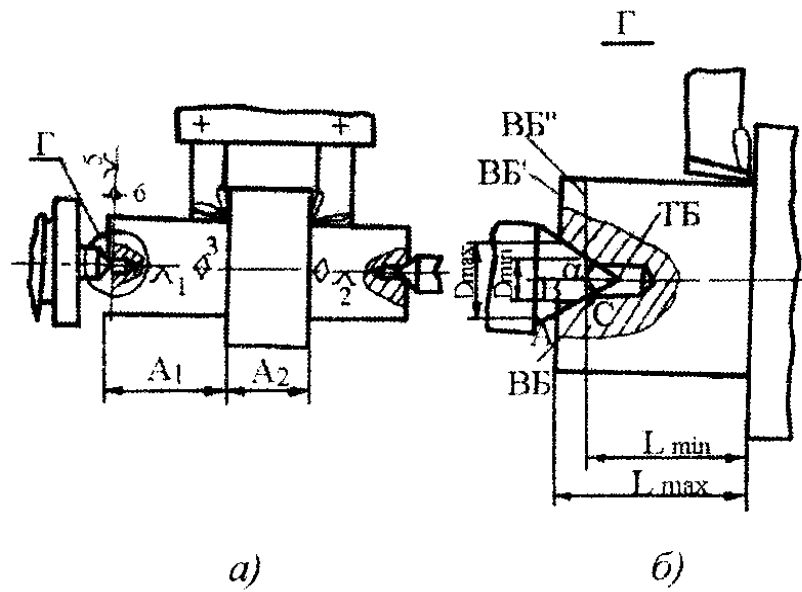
Схема встановлення вала в центрах на центрових оворах
